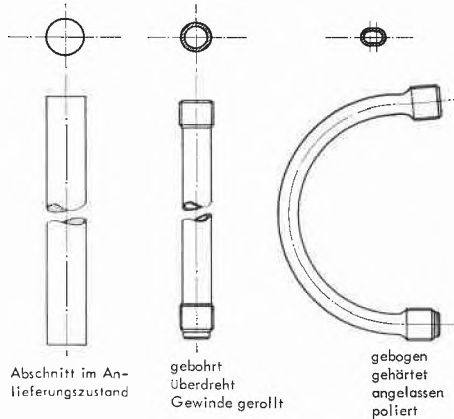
Die Bearbeitungsstufen einer Hydraulikfeder
